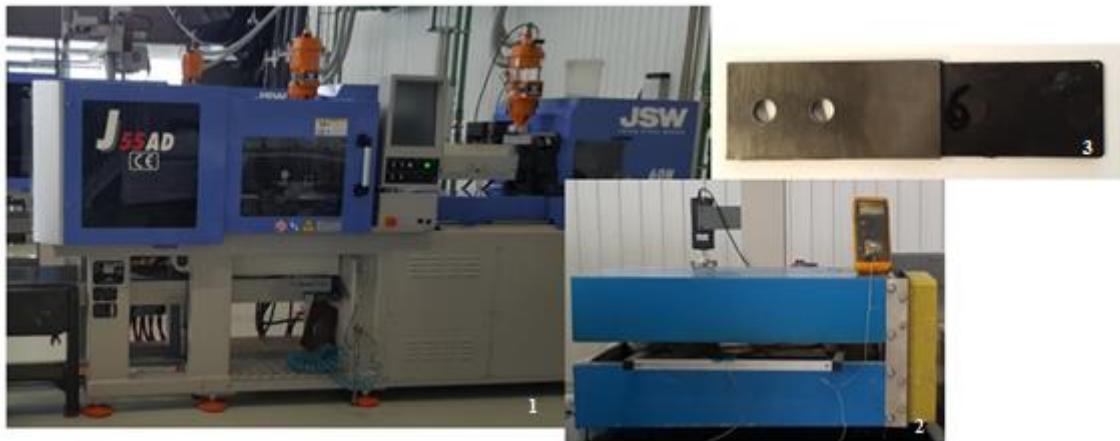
1- Máquina de injeção; 2 - Forno de aquecimento do laminado compósito; 3 - Provete resultante
